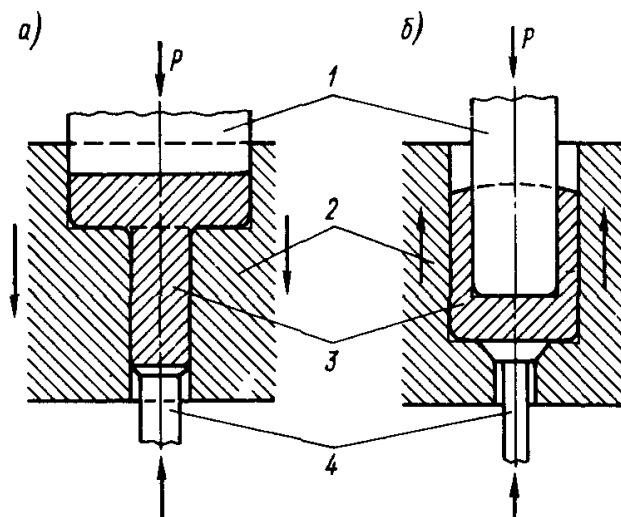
Схемы штамповки выдавливанием: а – прямое; б – обратное:
